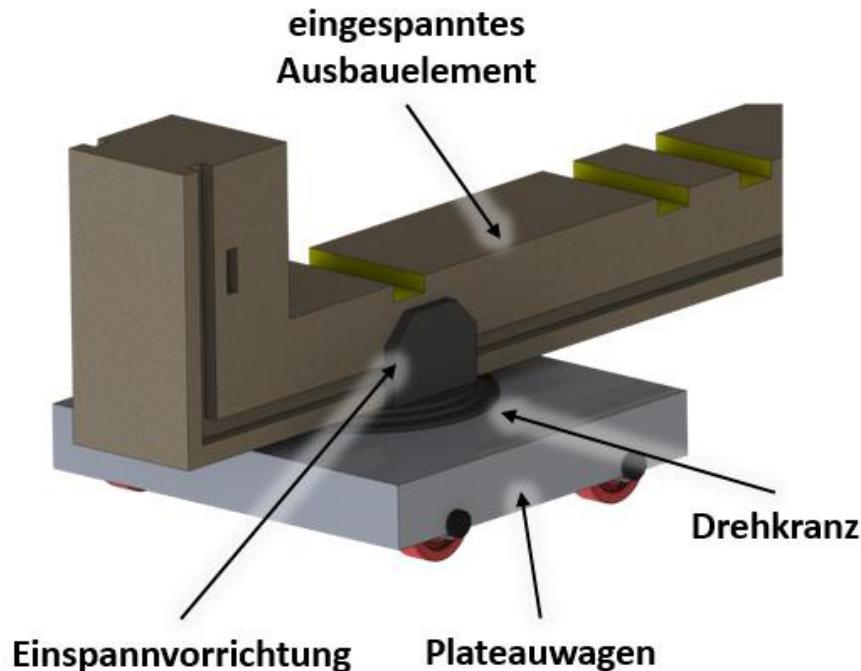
Seitliche Detailansicht des mit einem Ausbausegment beladenen Plateauwagens mit zusätzlicher Drehverbindung
